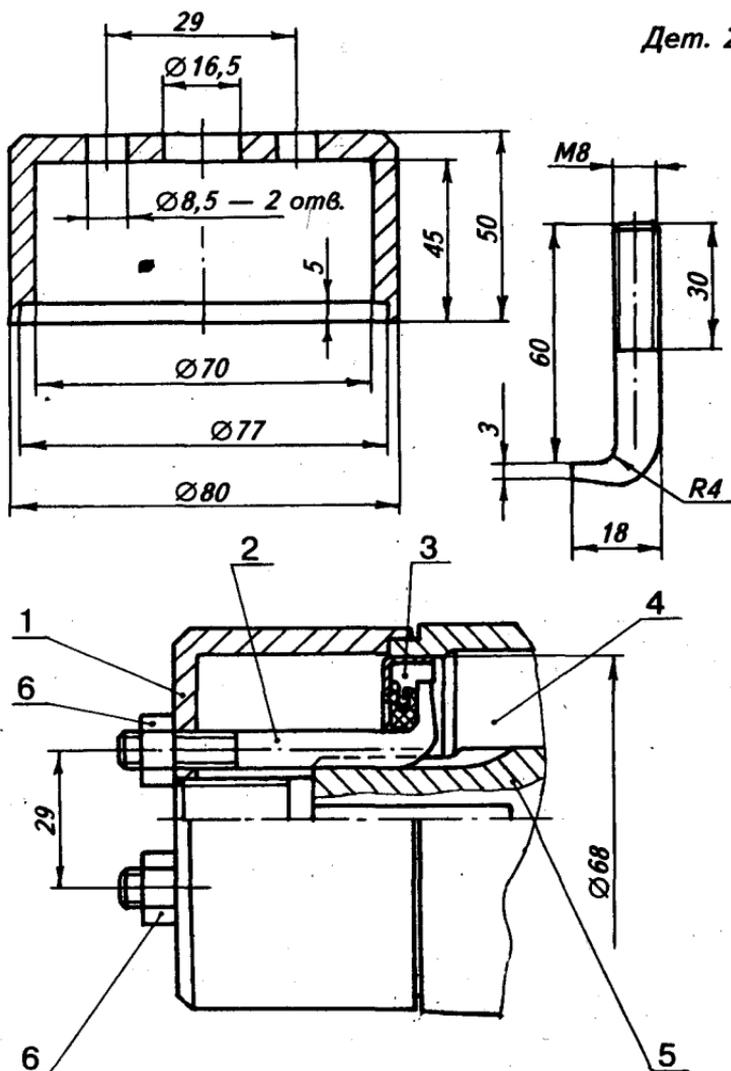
Приспособление для выпрессовывания сальника хвостовика: 1 — стакан; 2 — лапка (2 шт.), 3 — сальник; 4 — горловина картера редуктора; 5 — хвостовик (ведущая шестерня); 6 — гайка М8 (2 шт.).
